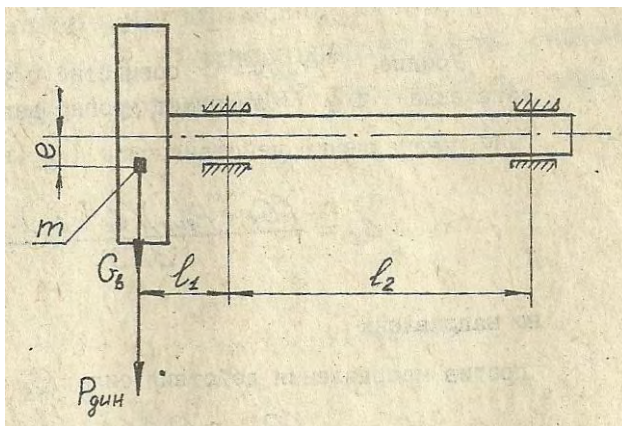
Расчетная схема неуравновешенного консольно закрепленного ротора с двумя подшипниковыми опорами
